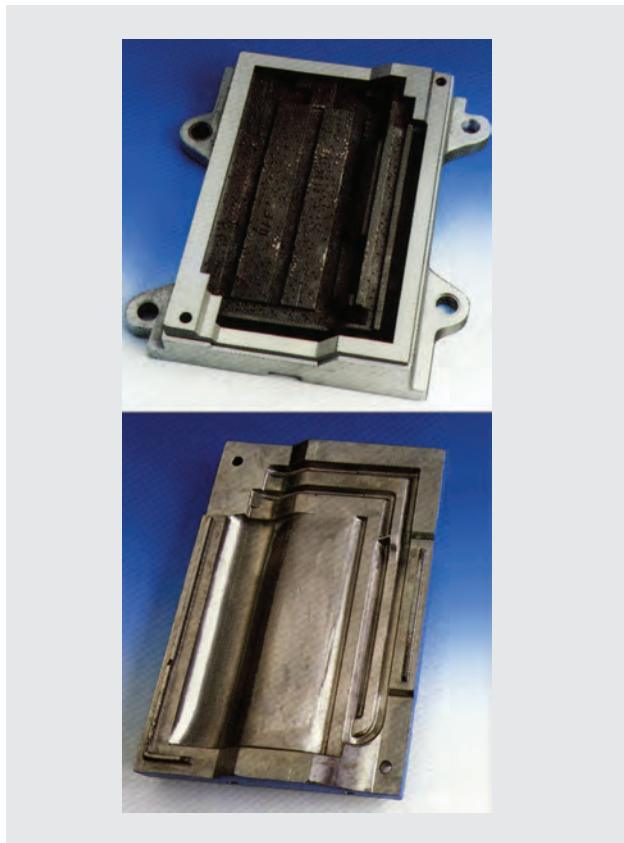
Arbeitsformen, oben für Gipsverpressung, unten Metallform aus CrNi-Stahl für die Verpressung mit Elektroshock oder anderen Trennmitteln z.B. Öl
